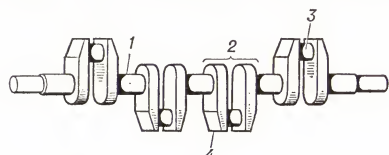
Коленчатый вал: 1 — коренная шейка; 2 — колено; 3 — шатунная шейка; 4 — щека.
